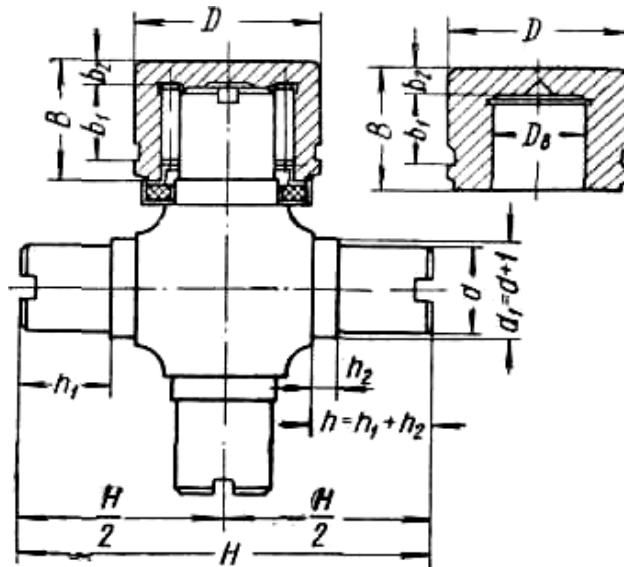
Розміри хрестовини і підшипника шарніра
